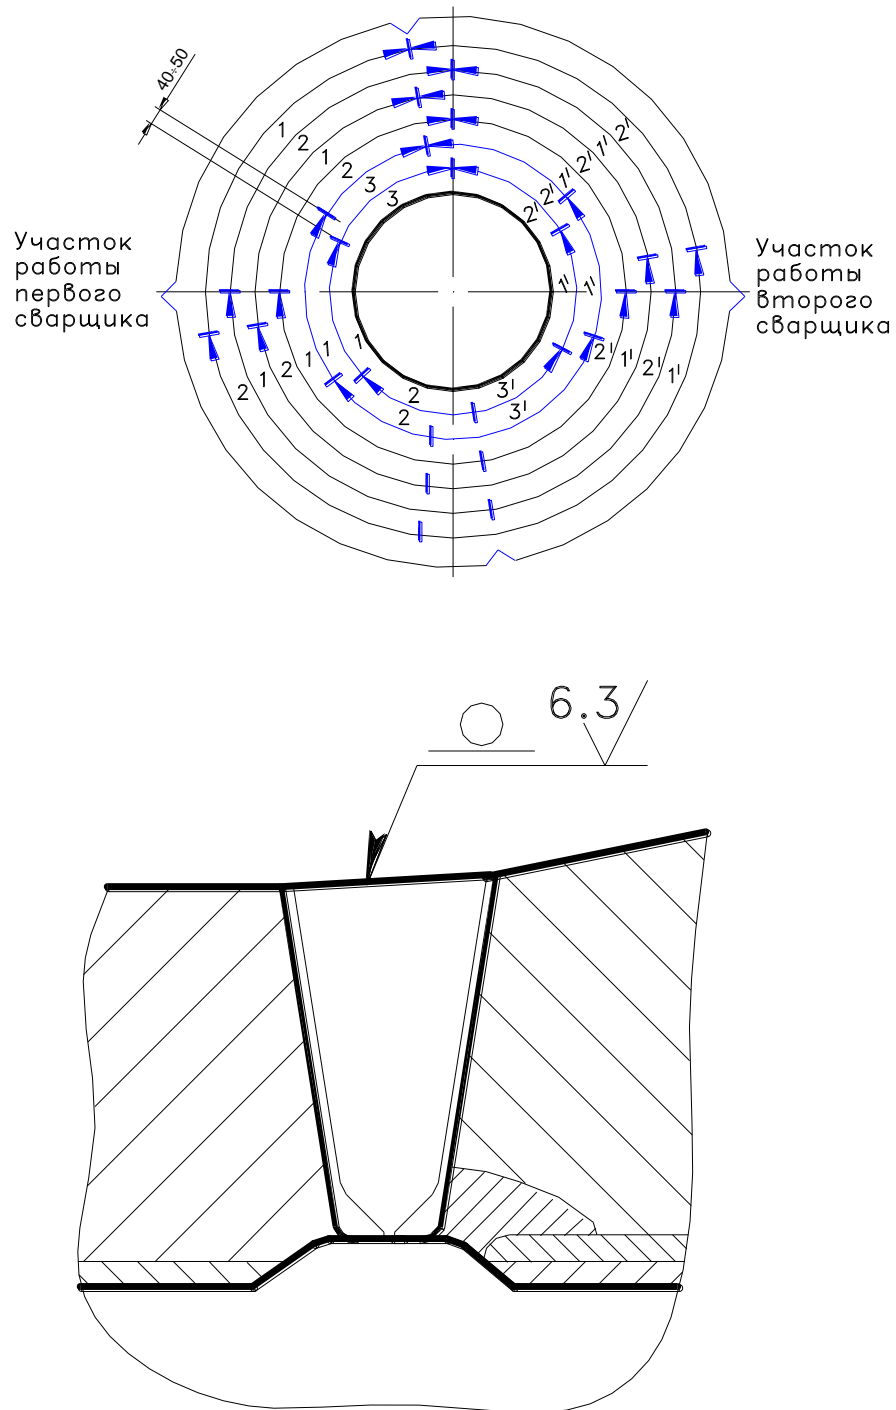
Порядок сварки и выполненное сварное соединение трубы узла трубного и патрубка реактора (до восстановления антикоррозионной наплавки)
